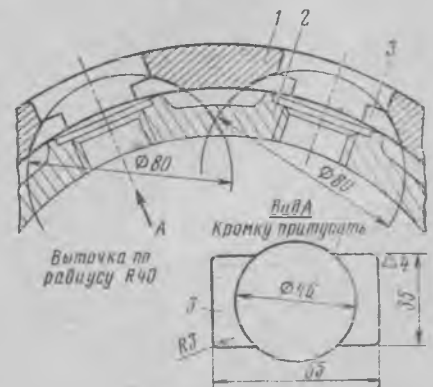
Изменения в конструкции рубашки: 1 — рубашка; 2 — гильза; 3 — выточки (фрезеровка) по адаптерным отверстиям рубашки
